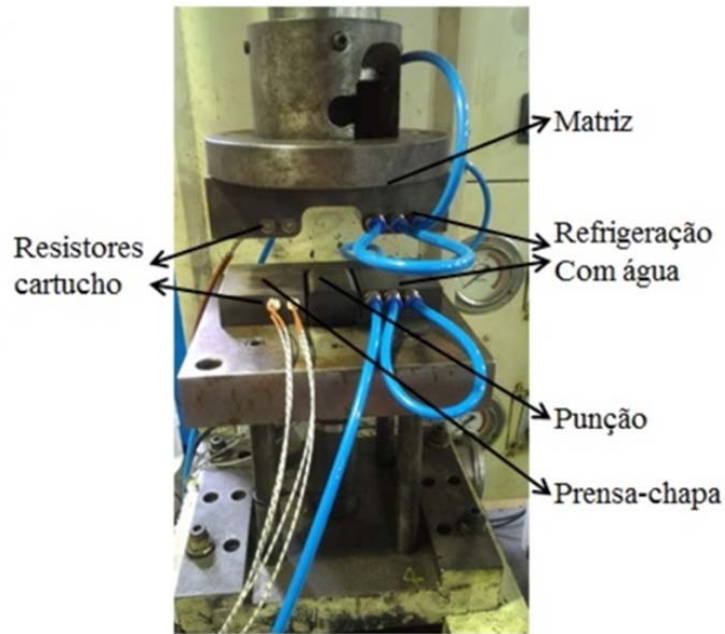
Detalhe da montagem das ferramentas de estampagem
